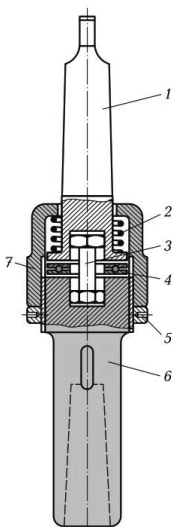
Свердильний патрон, що самовстановлюється: 1 – корпус; 2 – пружина; 3 – повідець; 4 – підшипник; 5 – стопорне кільце; 6 – оправлення; 7 – муфта
